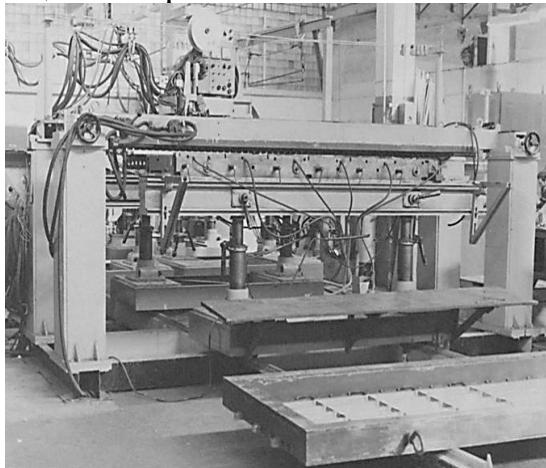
Внешний вид сварочного стапеля УСП-2.6
